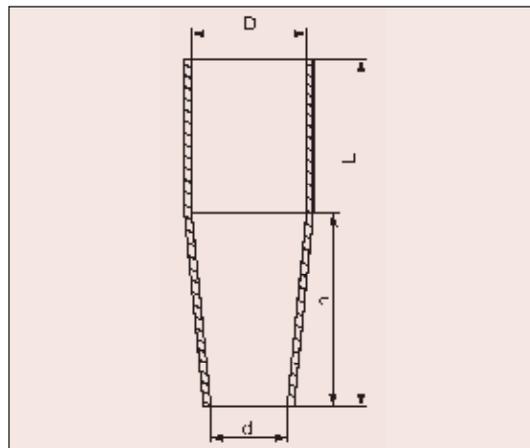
Геометрические размеры конусного сопла, обеспечивающего улучшенную защиту расплавленного металла при сварке в защитных газах (d = 0,70...0,85D; h = 1,5...2,0D; L = 3,0...3,5D)
